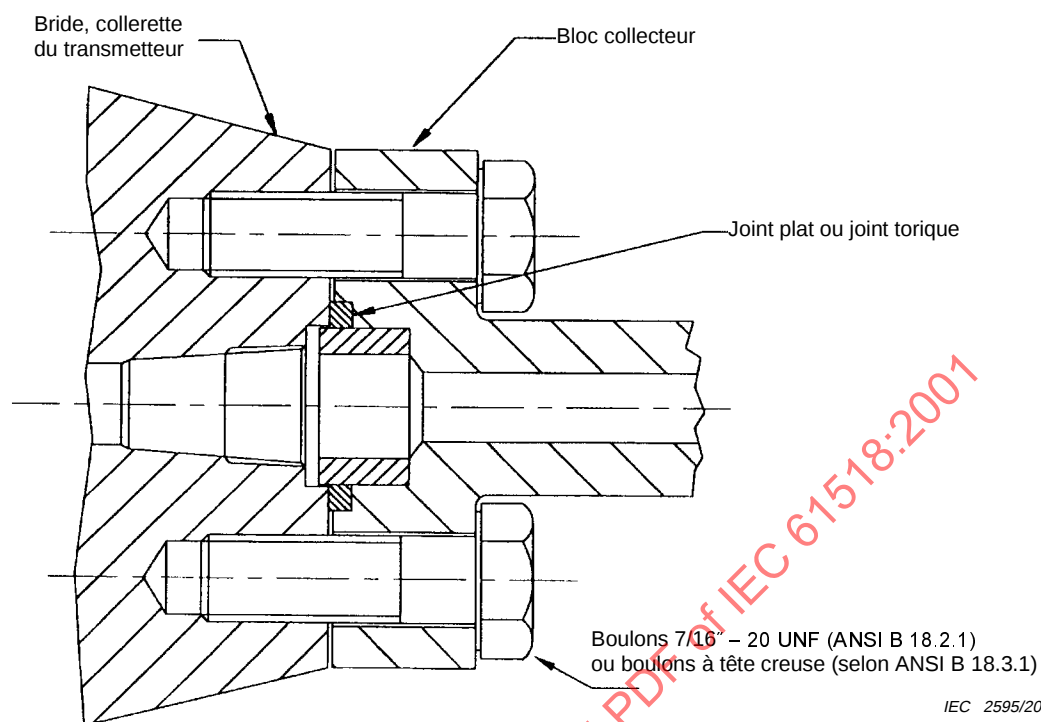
Connexion d'un collecteur type B (sans emboîtement) – Dimensions
